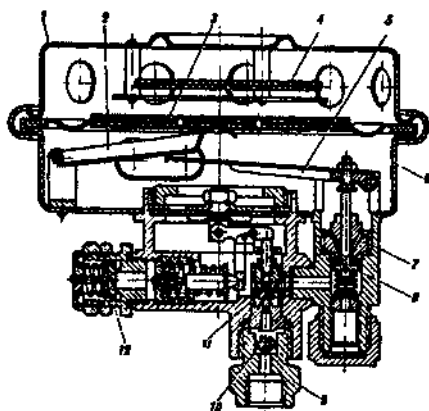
Дыхательный автомат аппарата АВМ-1М с редуктором:
